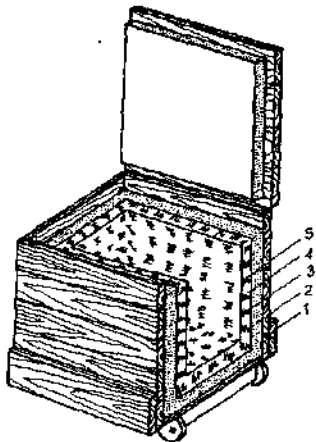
, Ледник для подвала: 1 — деревянный ящик; 2 — опилки или минеральная вата; 3 — металлический бак; 4 — лед; 5 — бак из пластмассы или жести
